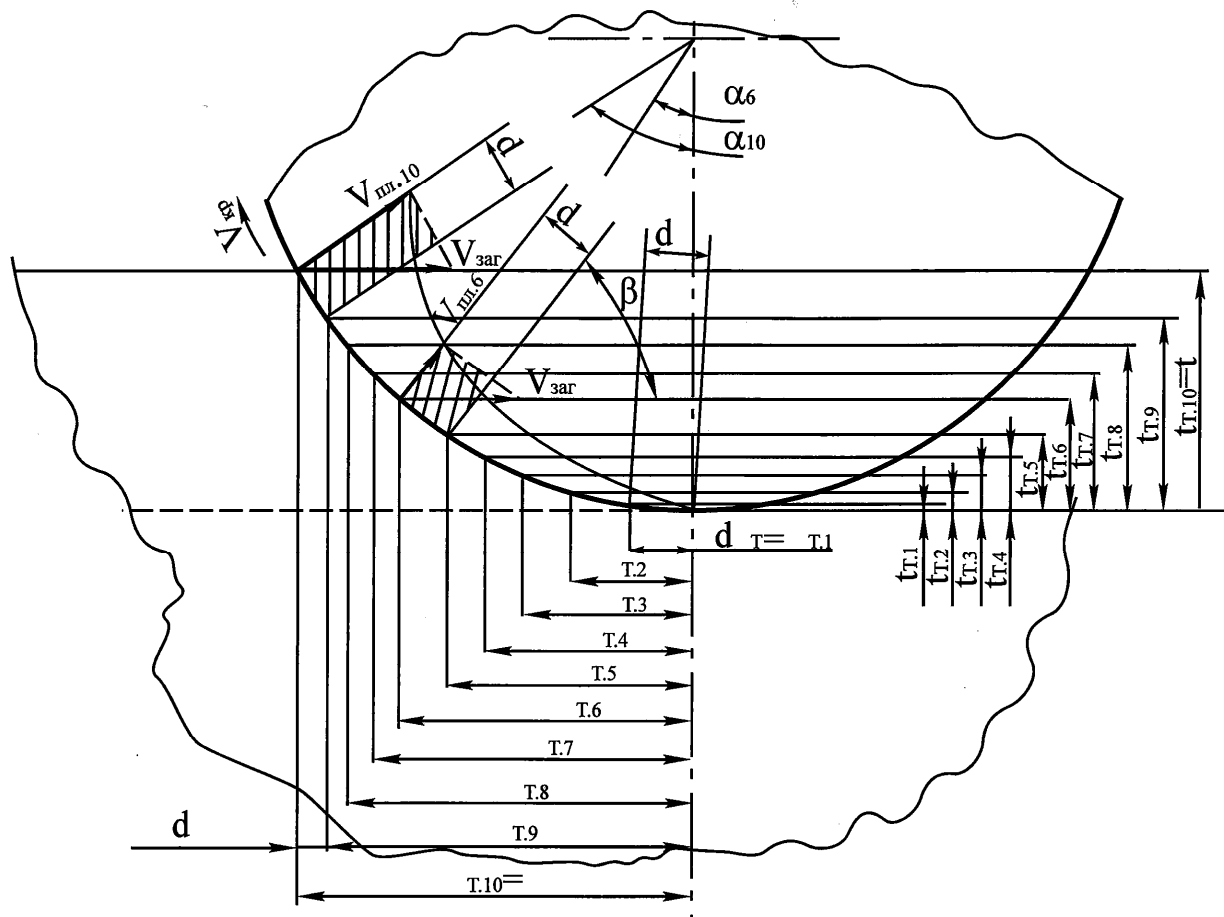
Схема внедрения металла в рабочую поверхность круга.
